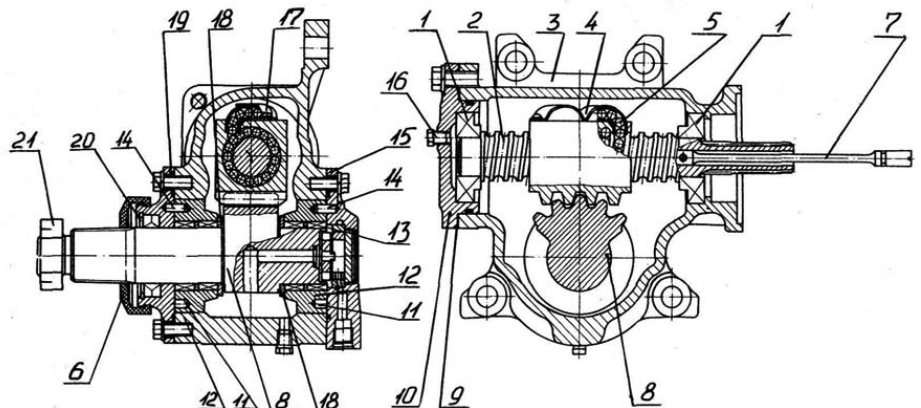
Рулевой механизм: 1 — подшипники; 2 — винт; 3 — корпус; 4 — гайка-рейка; 5 — шарики; 6 — уплотнитель; 7 — торсион; 8 — зубчатый сектор; 9 — регулировочные прокладки; 10 — крышка; 11 — отверстия; 12 — эксцентриковые вкладыши; 13 — подшипник скольжения; 14 — штифт; 15 — крышка (клапан ограничения давления); 16 — пробка; 17 — прижим; 18 — упорное кольцо; 19 — крышка; 20 — манжета; 21 — гайка
